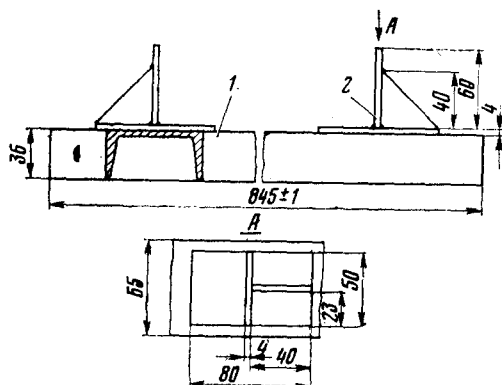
Вспомогательное приспособление для демонтажа коробки передач
